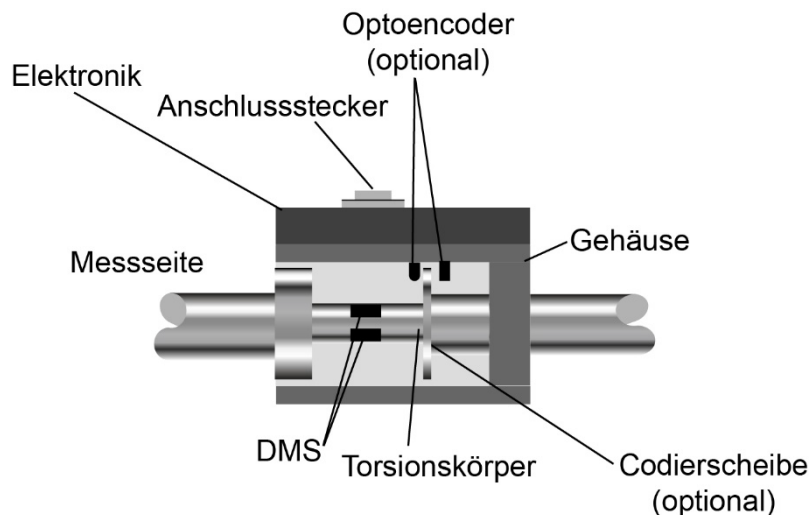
Prinzipieller Aufbau des Drehmomentsensors Typ 8656
